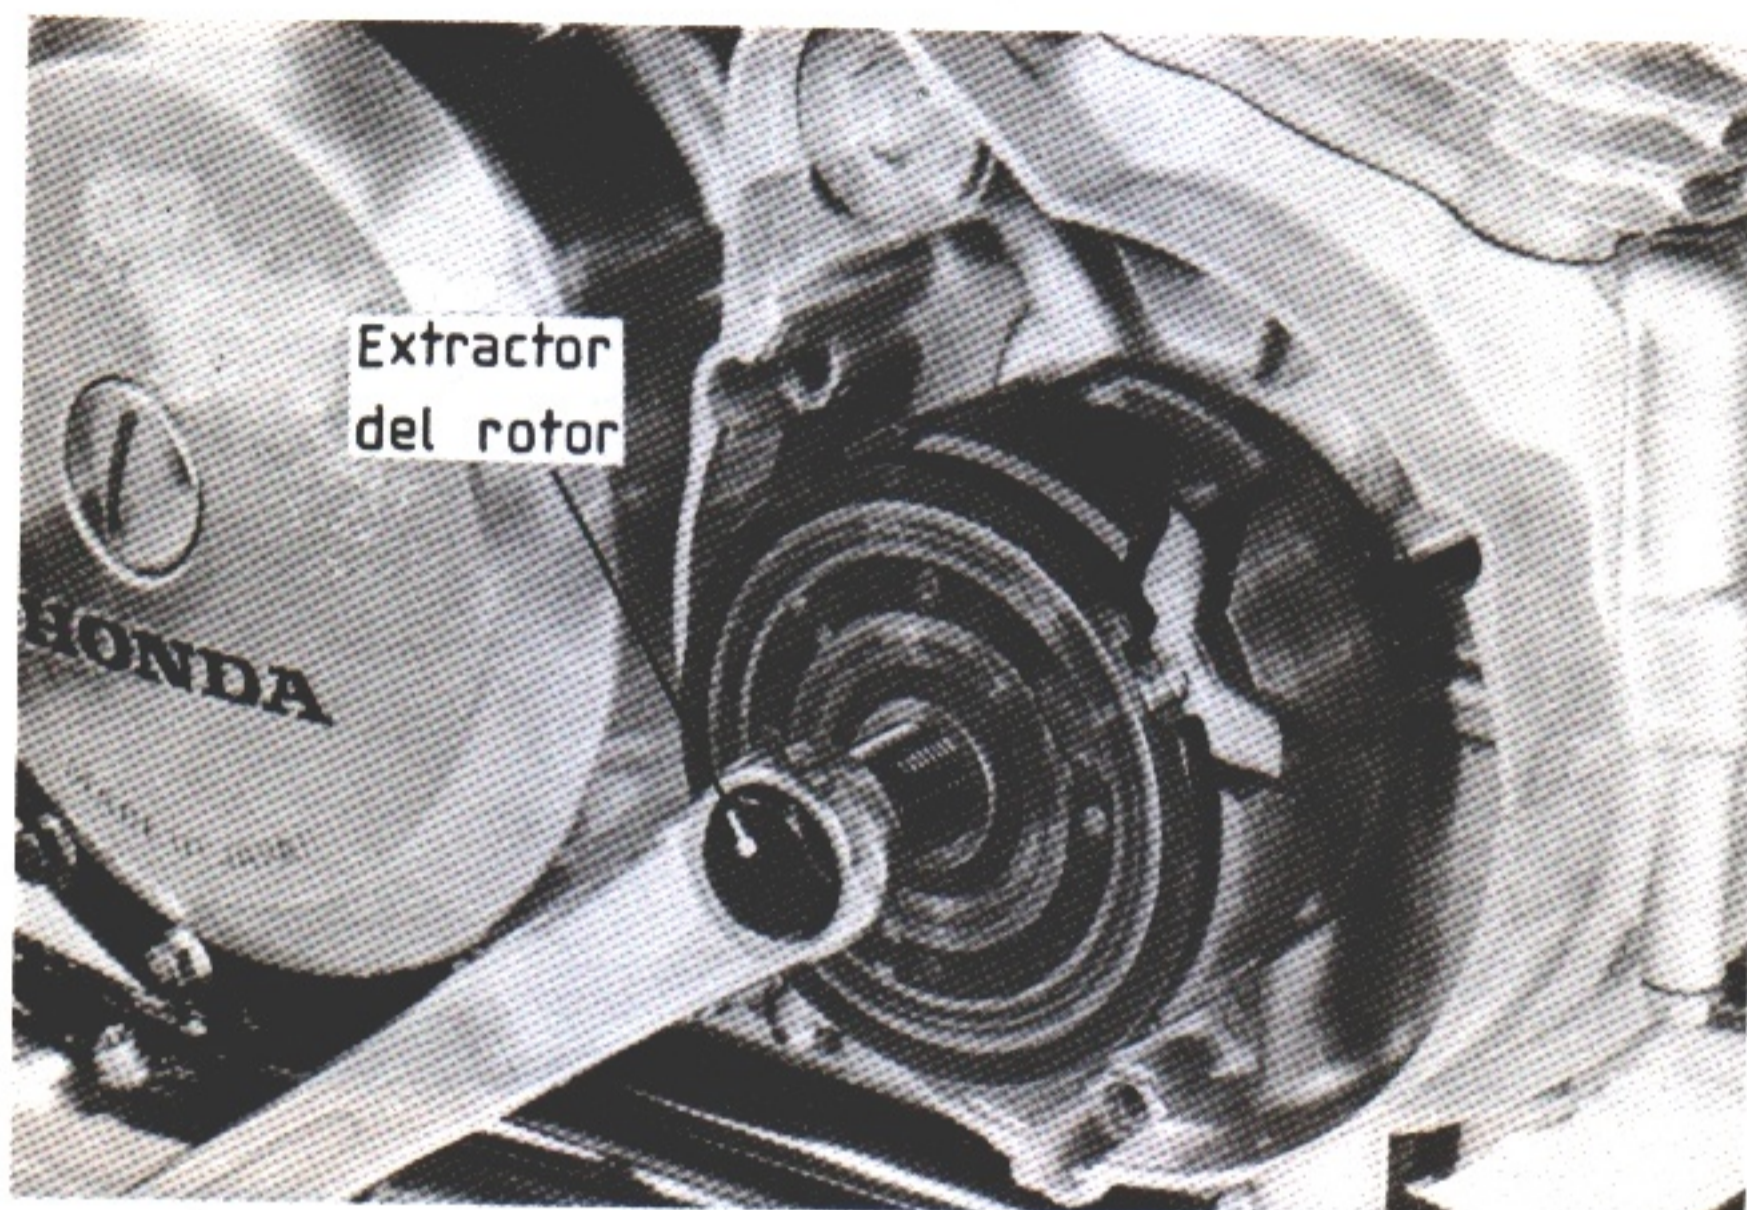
Desmontaje del rotor con la ayuda de un extractor.
